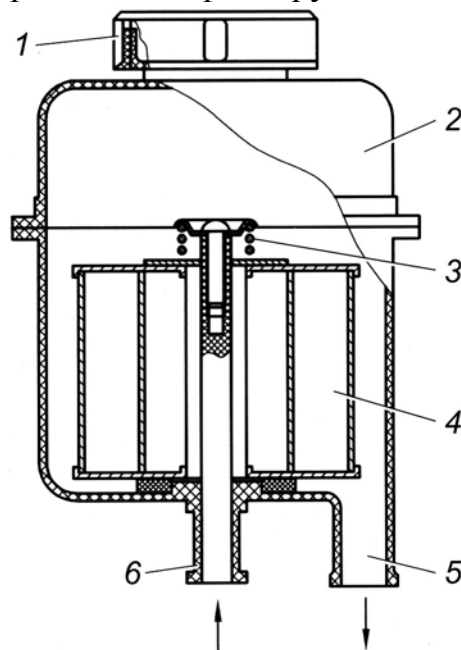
Неразборный бачок системы ГУР: 1 – крышка; 2 – корпус; 3 – пружина клапана; 4 – фильтрующий элемент; 5 – боковой патрубок; 6 – центральный патрубок
